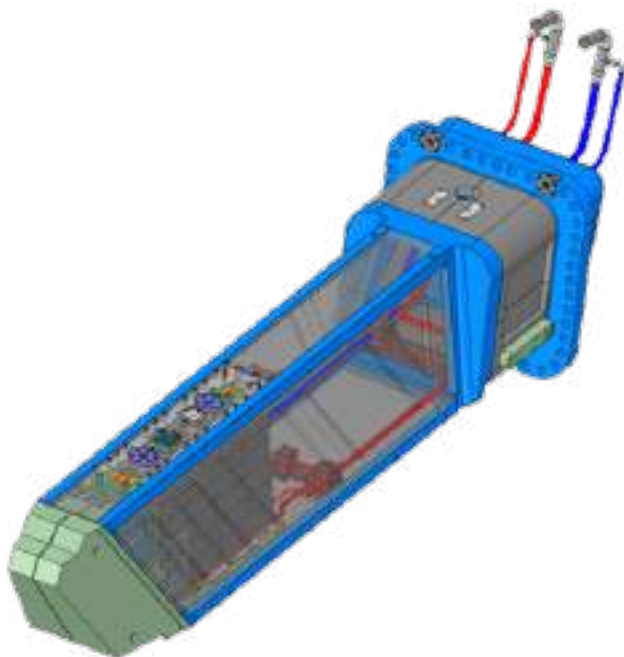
Чертеж порт-плага верхнего порта № 07 ИТЭР для предварительной защиты проекта. Спереди расположена обращенная к горячей плазме диагностическая передняя стенка (зеленый цвет), синим цветом показан корпус порт-плага. Передняя стенка и корпус будут изготовлены и поставлены в институт сторонними организациями. Институт будет изготавливать внутреннее наполнение порт-плага и производить сборку всего порт-плага.
